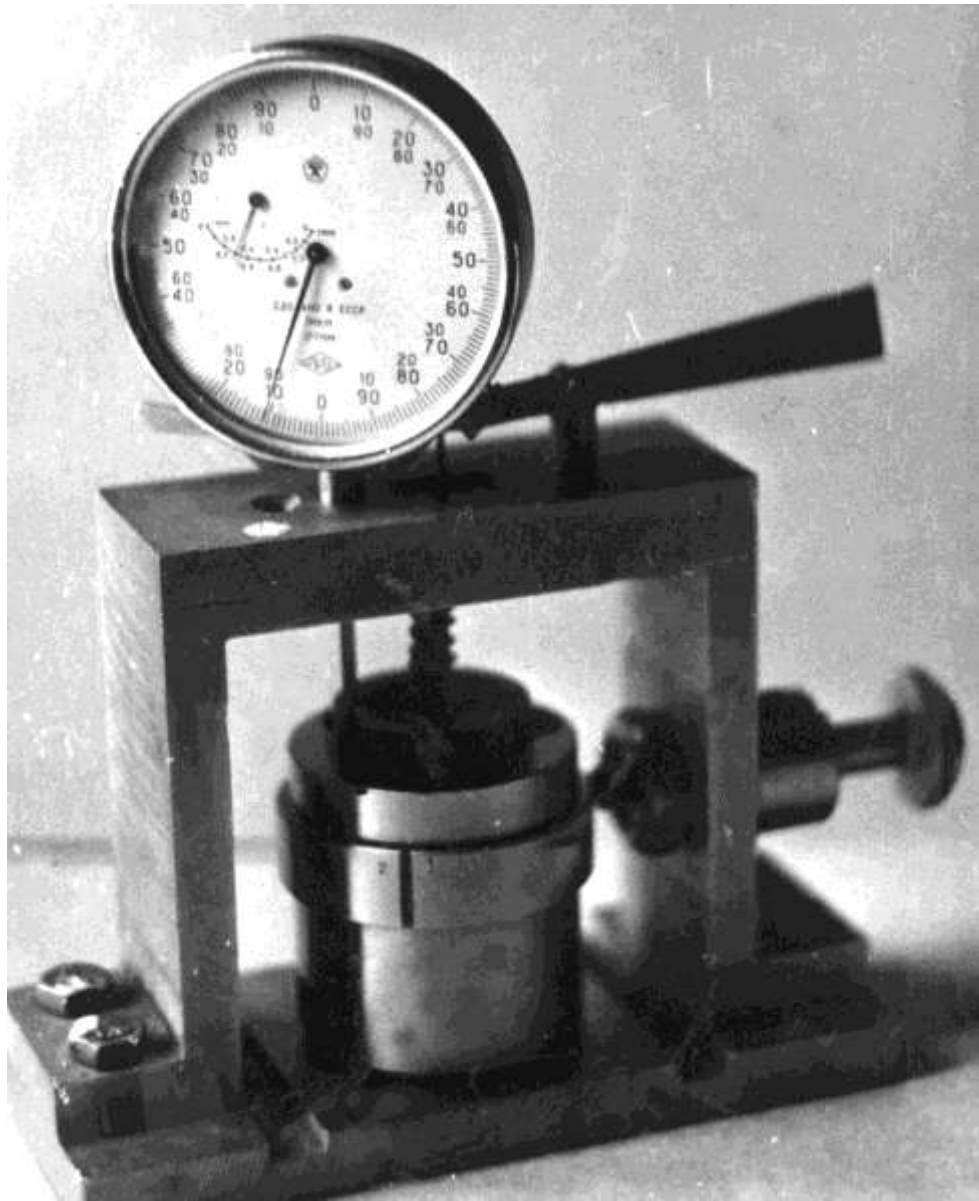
Контрольний пристрій для вимірювання величини зносу
